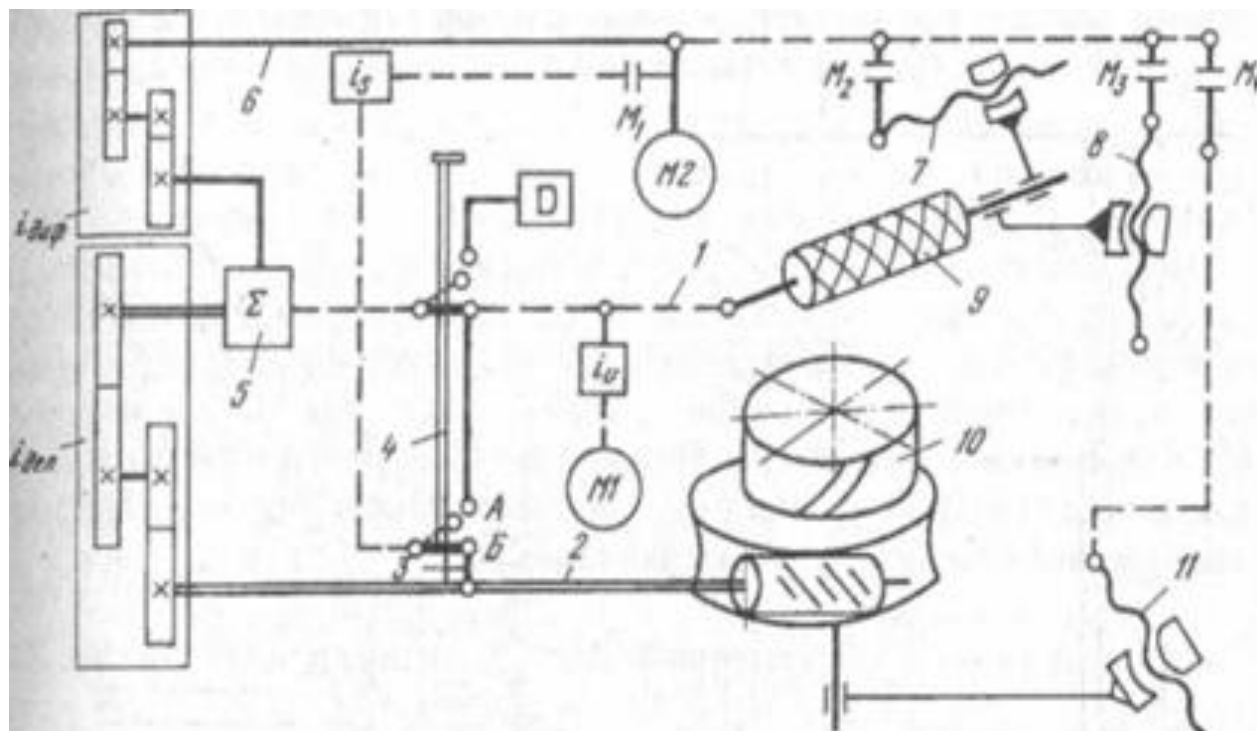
Кинематическая структура зубофрезерного станка.
